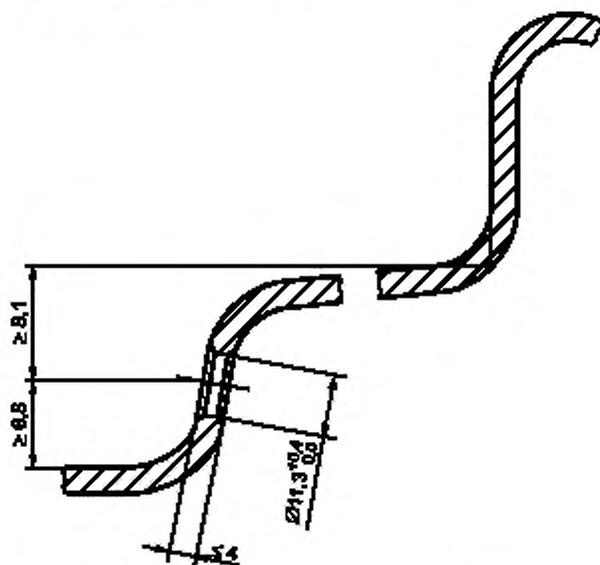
Размеры вентиляного отверстия для бескамерных шин
